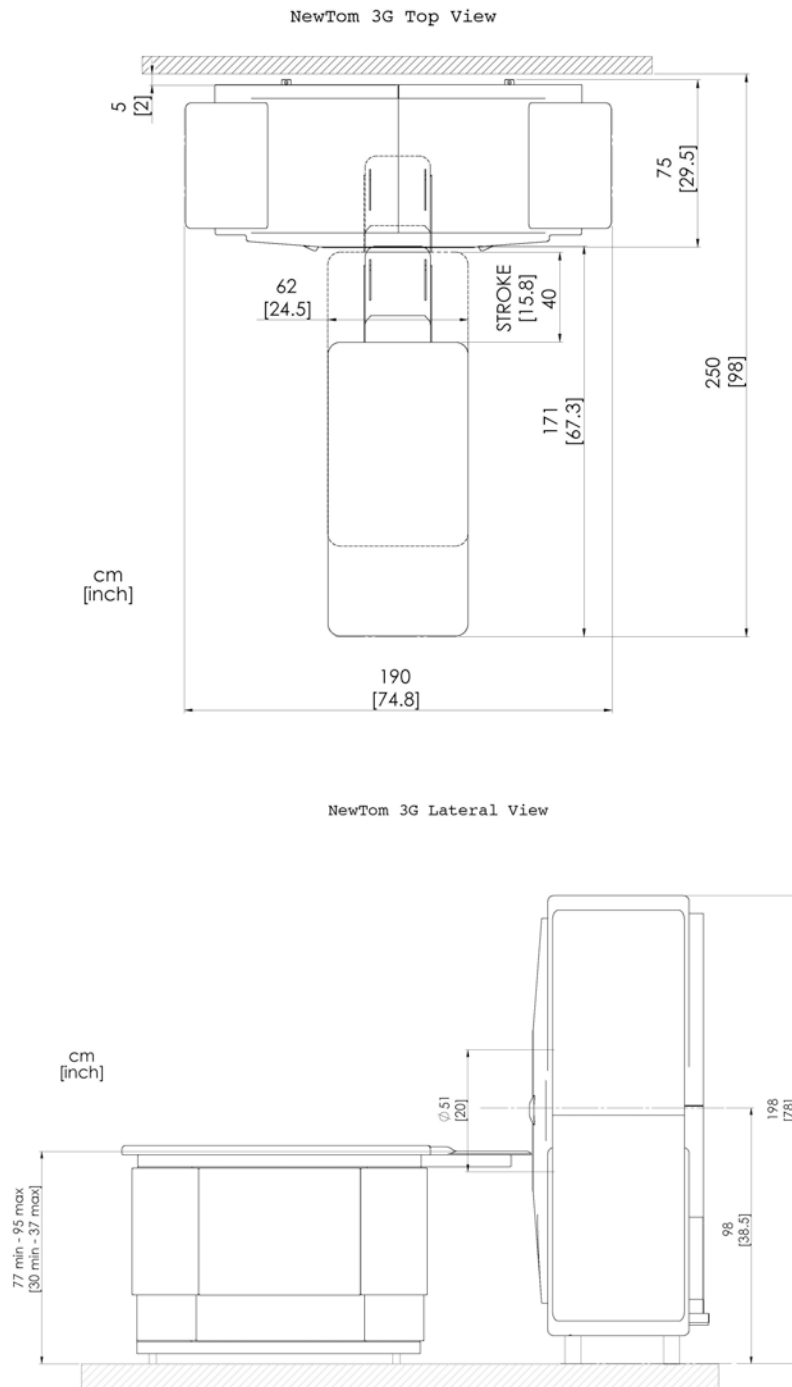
Technische Zeichnungen mit Abmessungen der NewTom 3G
